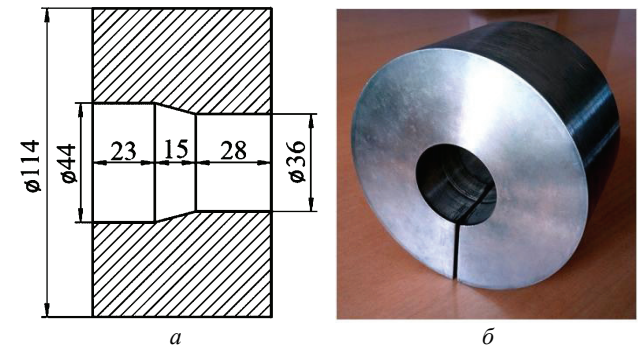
Массивный одновитковый соленоид: а – чертеж, б – фото
